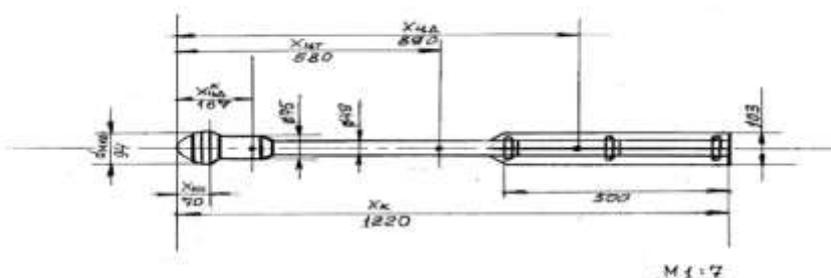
Чертёж корпуса ракеты и положение её центра тяжести
